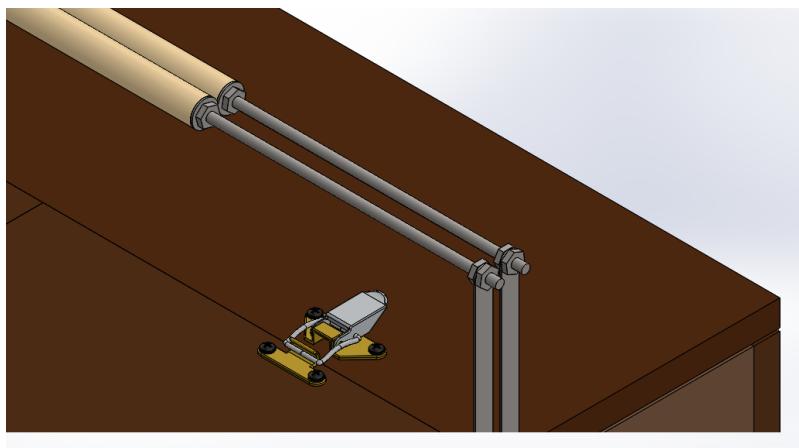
Detalhe da montagem da alça e sua fixação nas dobradiças laterais
